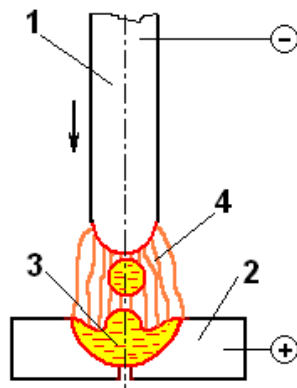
Схема сварочной дуги постоянного тока: 1 – электрод;
